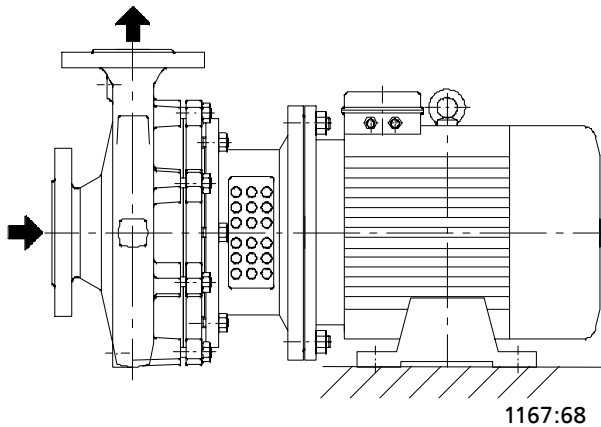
Motorfuß Befestigung unten, Motorgröße 132 = 5,5 kW bis 225 = 45 kW
